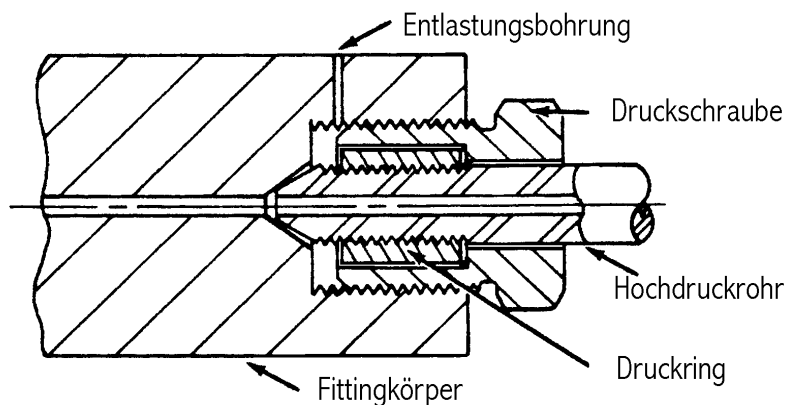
Skizze einer Standard-Hochdruckverschraubung [386].
